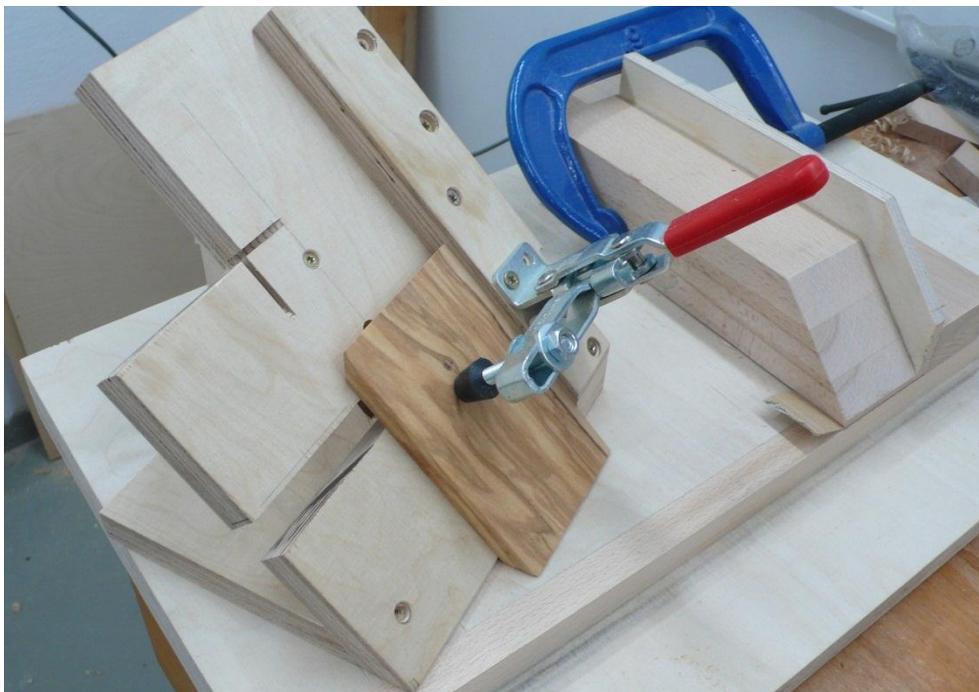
Jig für das Fräsen der Nuten und Stoßlade
